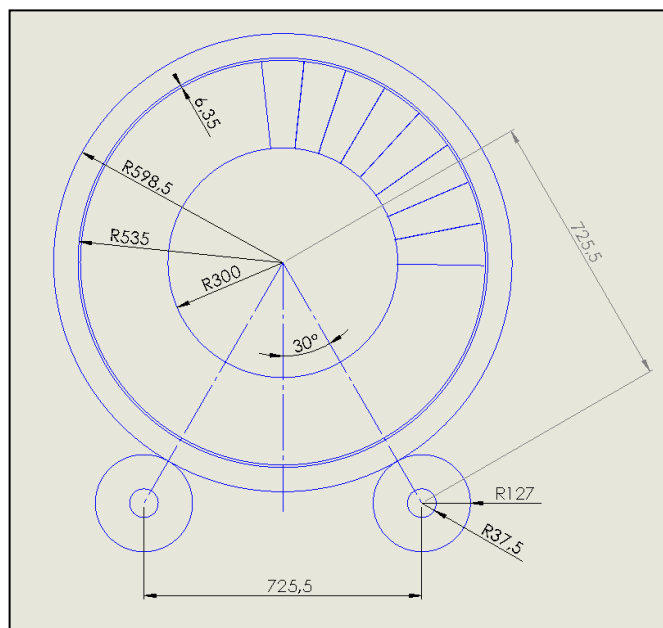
Vista frontal del cilindro. Unidades: milímetros (mm).
